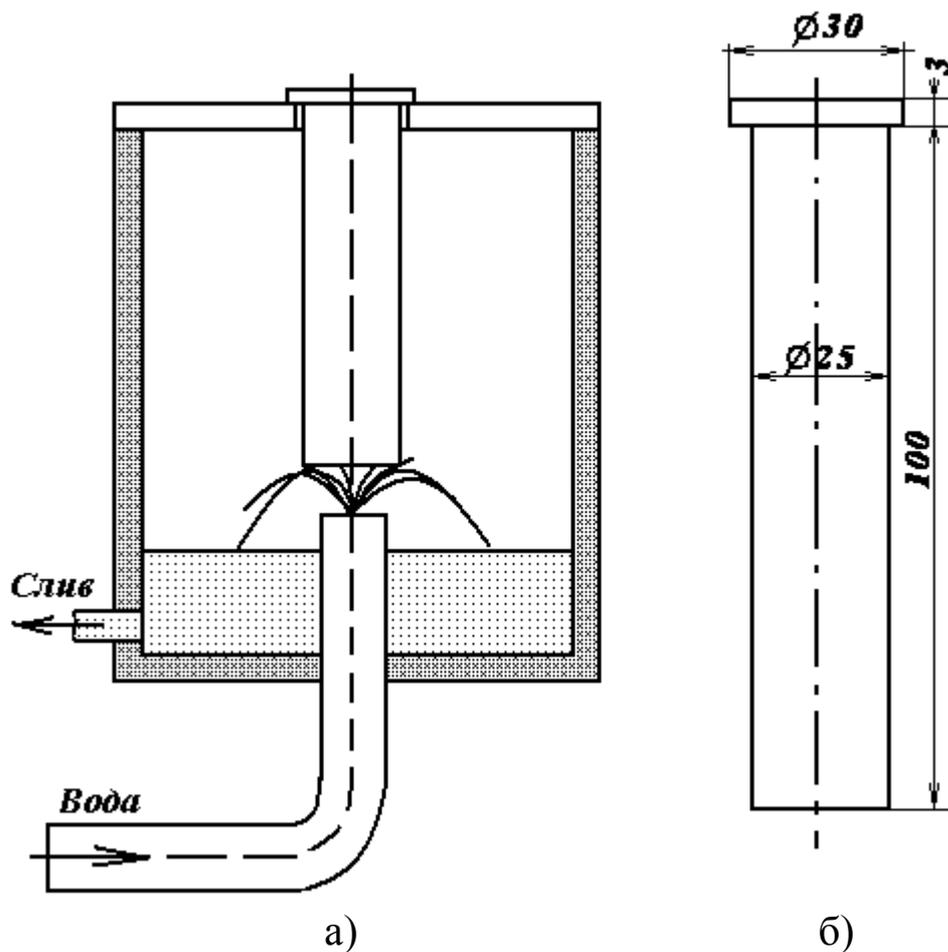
Установка (а) и образец (б) для торцевой закалки.
